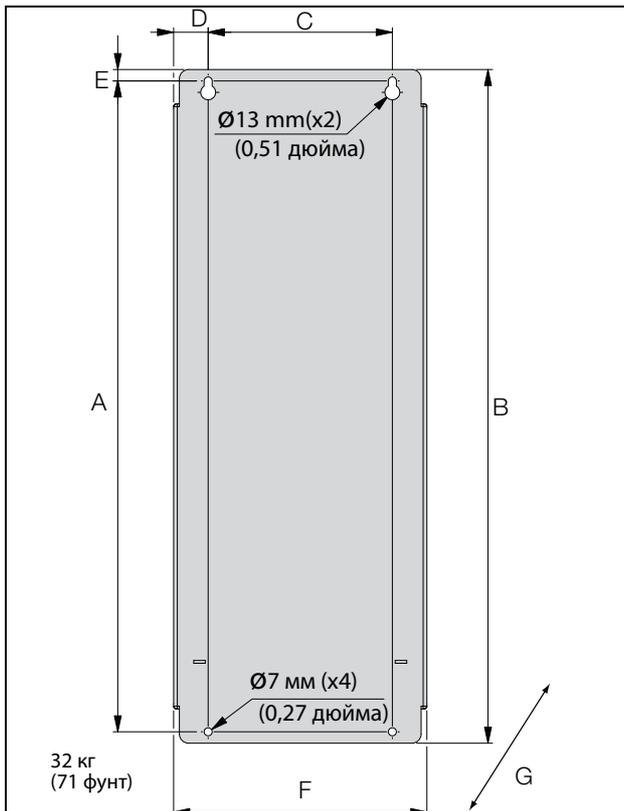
Устройство Emotron FDU моделей с 48/52-061 по 074 (размер корпуса D), моделей с 69-033 по 69-058, (размер корпуса D69).
